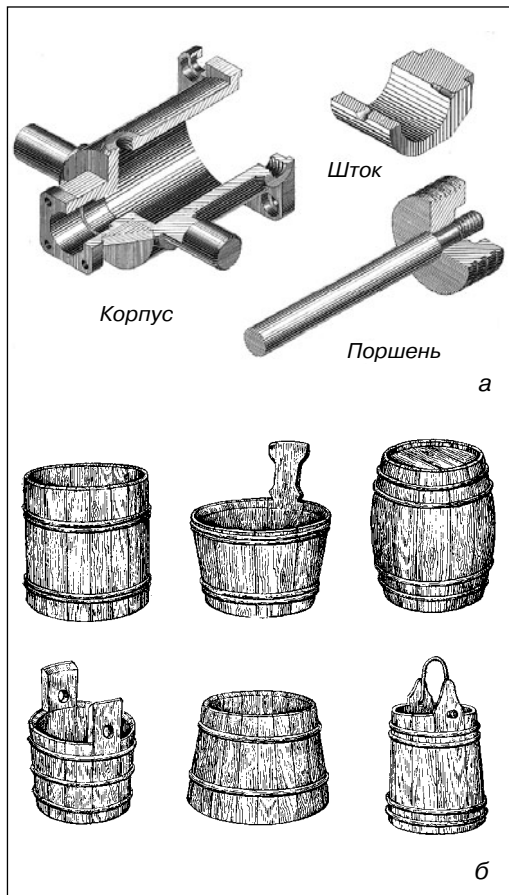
Штриховка: а) детали клапана; б) новгородские бондарные изделия из раскопок
